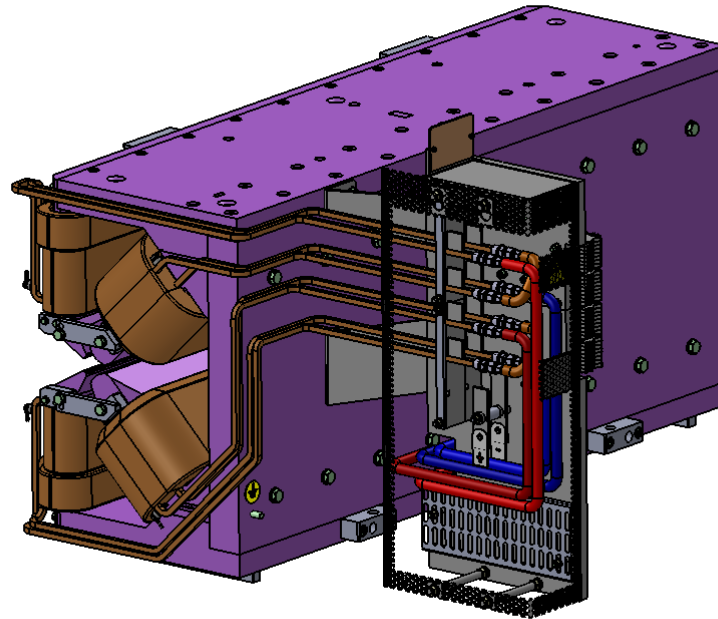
Эскизный вид диполь-квадрупольного магнита
